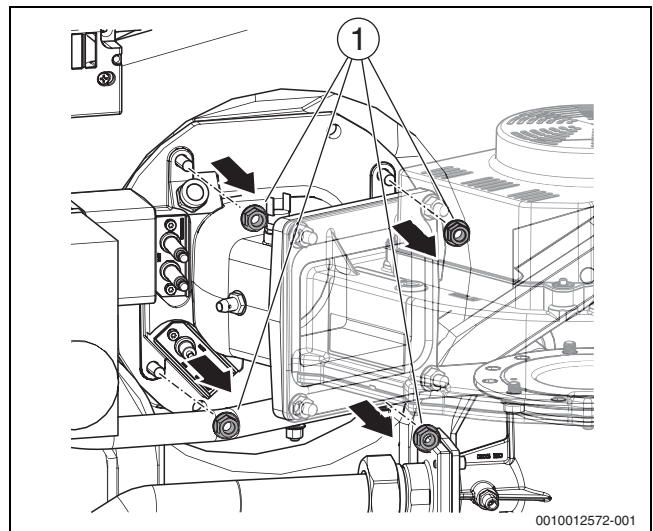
Desserrage de l'écrou du mélangeur coudé
